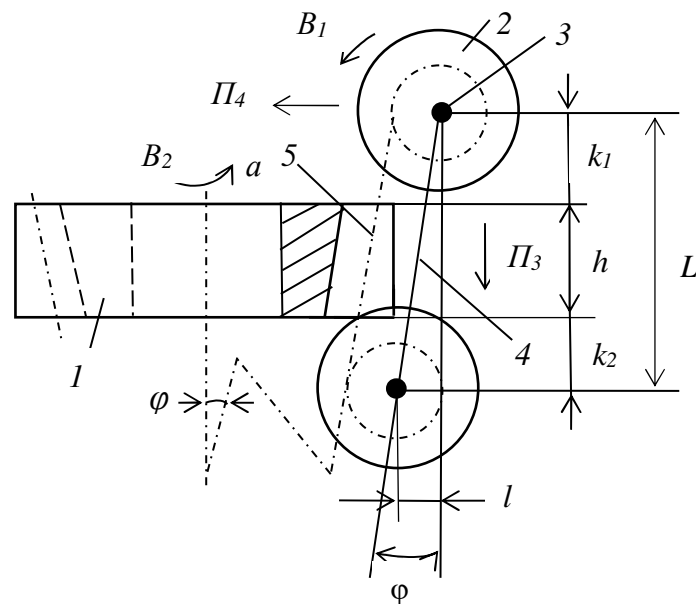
Способ фрезерования цилиндрических зубчатых колес с наклонными зубьями
